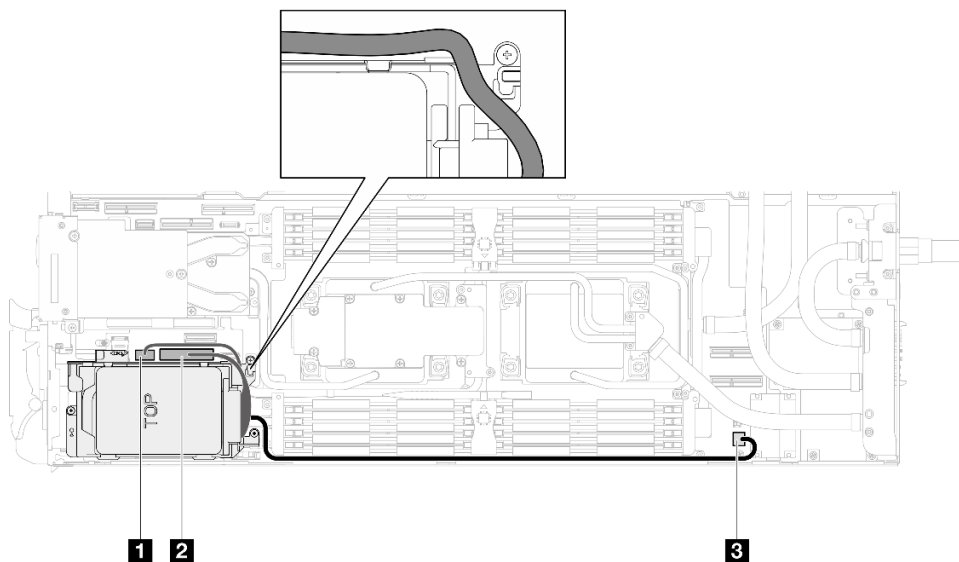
Cheminement des câbles du bloc unité NVMe 7 mm
